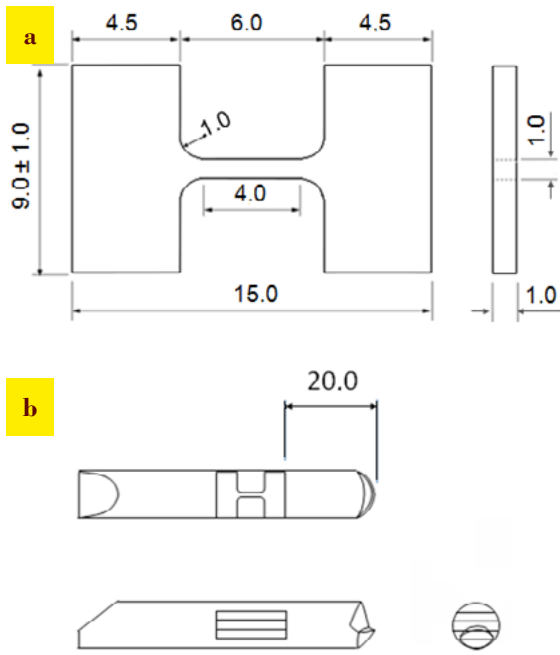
Esquemas de la probetas subescaladas de tracción: (a) Dimensiones y (b) Posición de maquinado de las probetas. Cotas en mm.
